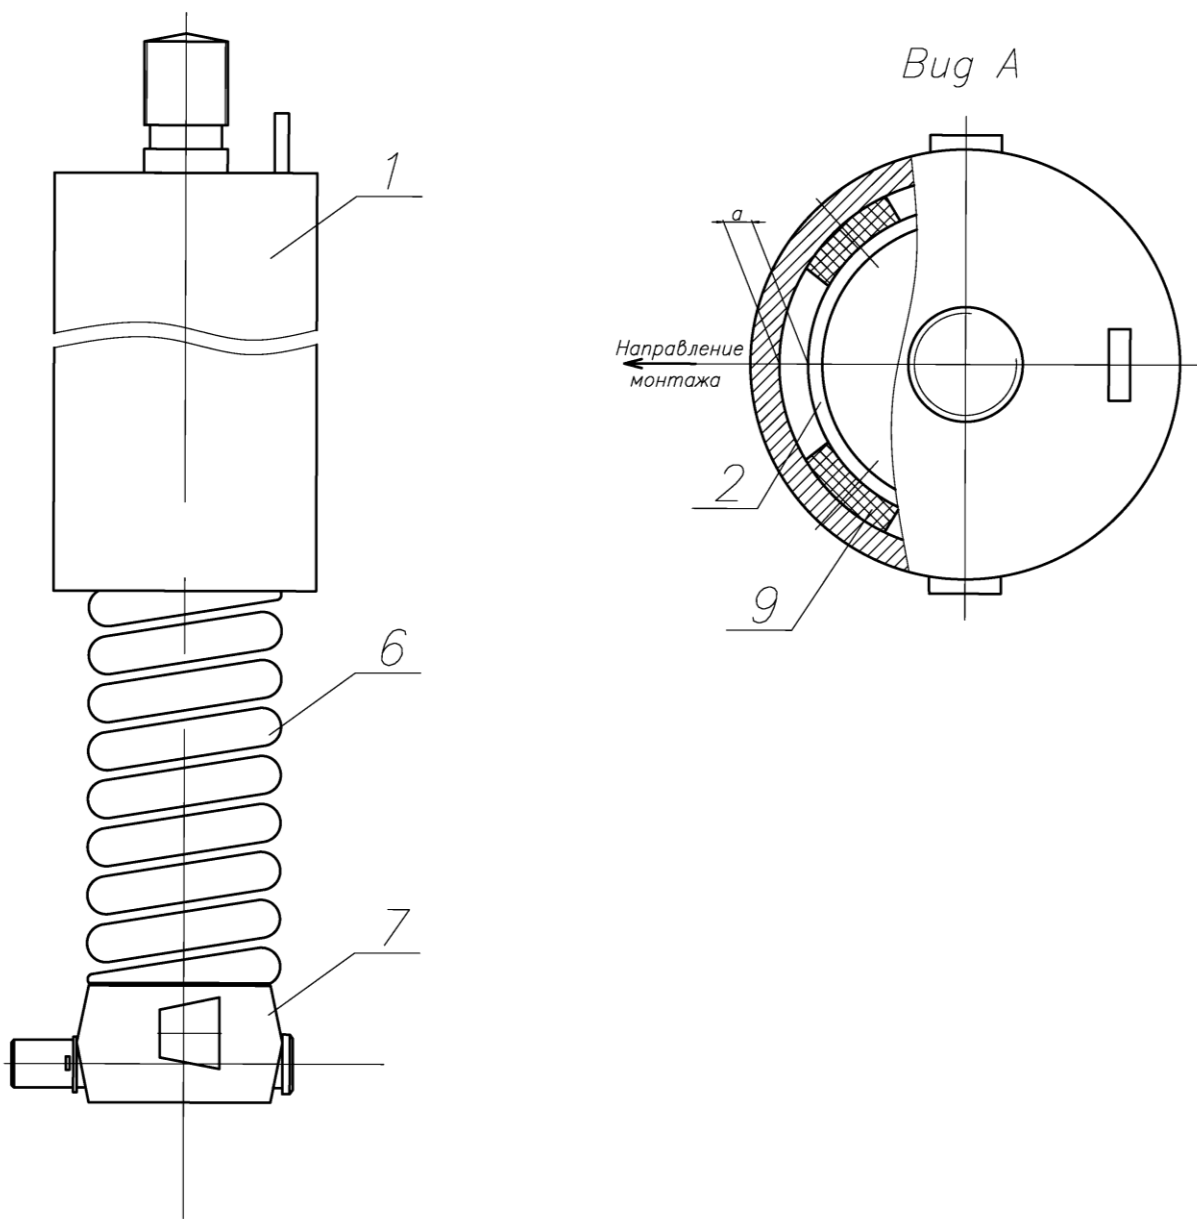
Фрикционный буксовый гаситель колебаний типа А в сборе
